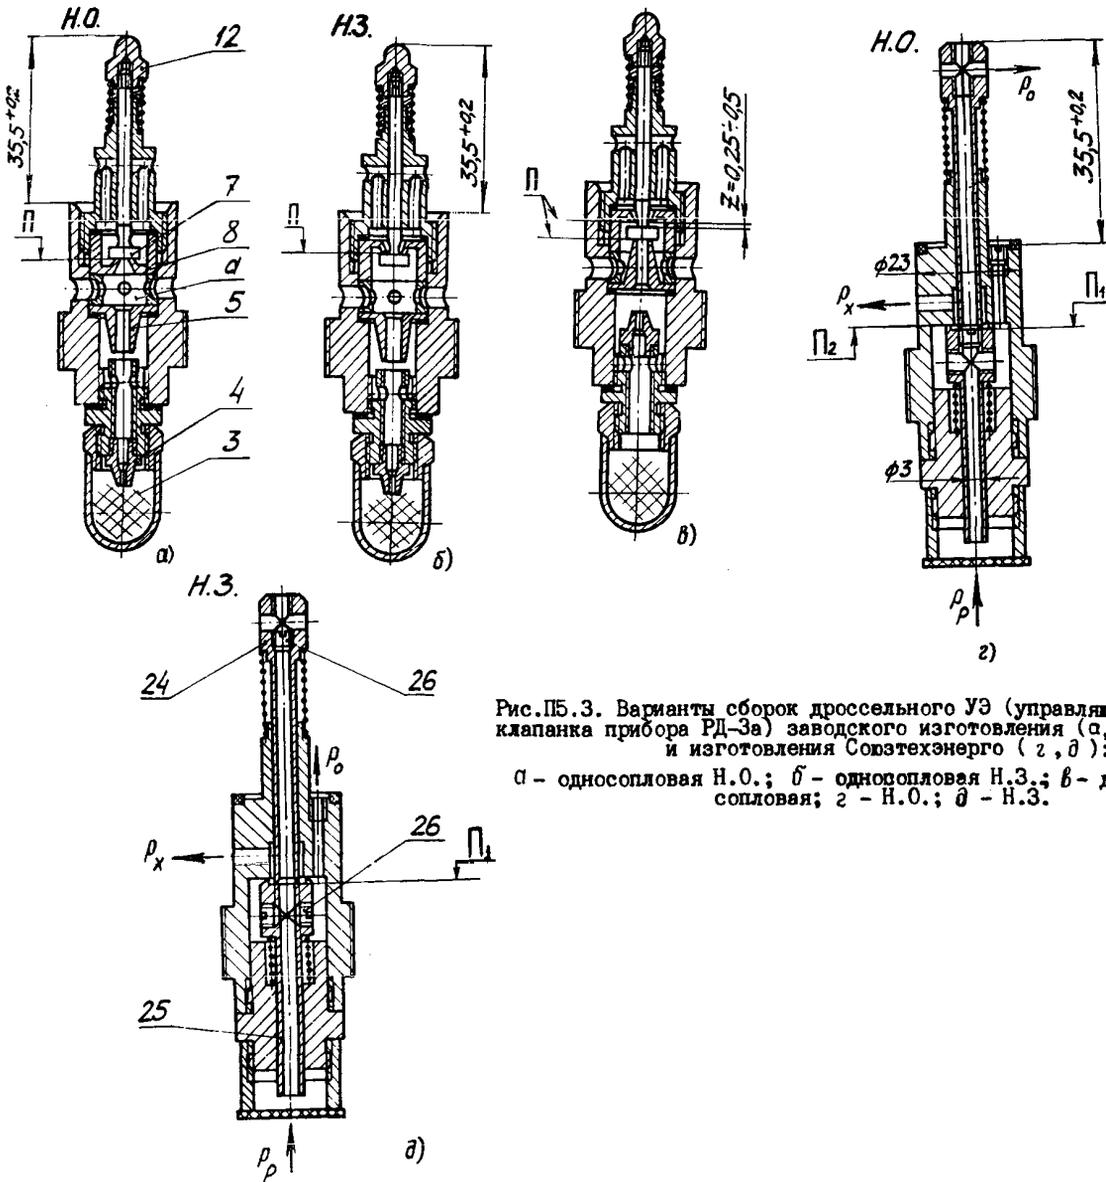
Варианты сборки дроссельного УЭ (управляющего клапанка прибора РД-3а) заводского изготовления (а, б, в) и изготовления Совтехэнерго (г, д):
